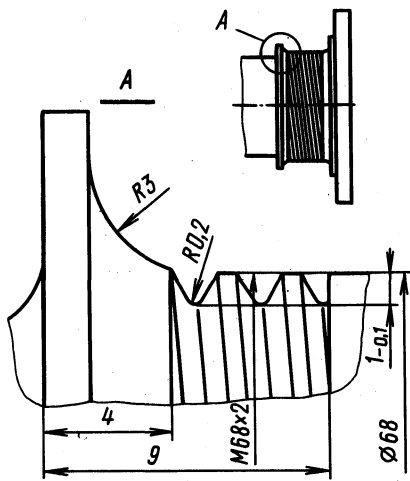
Задний конец коленчатого вала двигателя ЗМЗ с нарезанной маслосгонной резьбой
